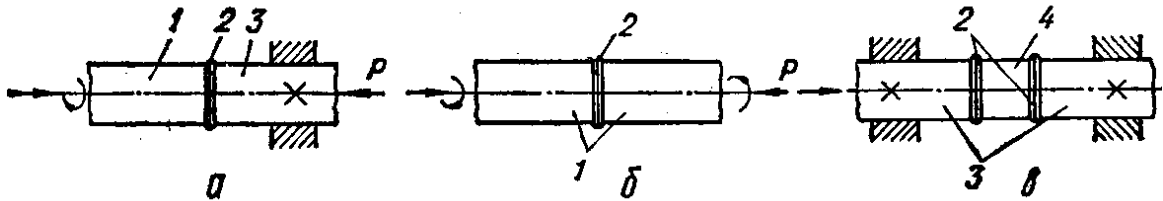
Схеми зварювання тертям з використанням обертання : а-1 деталі; б-2-х деталей; в-вставки. 1-деталь, яка обертається; 2-шов; 3-нерухома деталь; 4-вставка.
